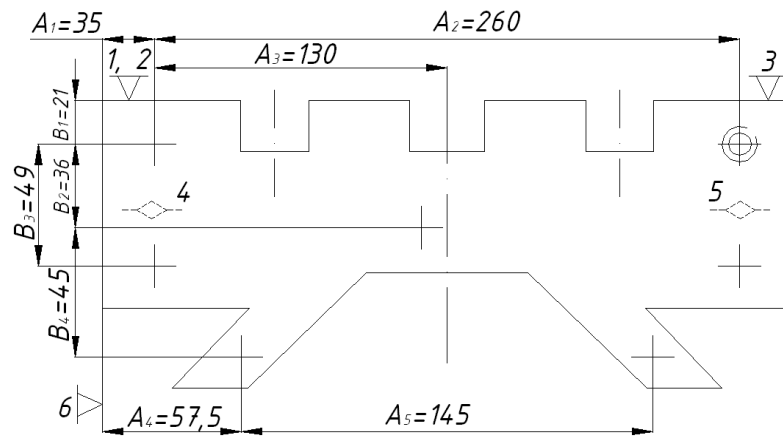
Схеми базування для оброблення отворів 40 і 42
